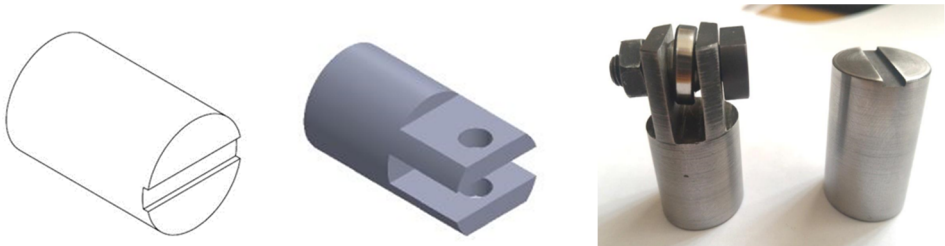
Тримачі для шарнірних підшипників ковзання з внутрішнім діаметром обойми 6 мм, що встановлюються на установці виготовленій згідно ГОСТ 23.211-80
